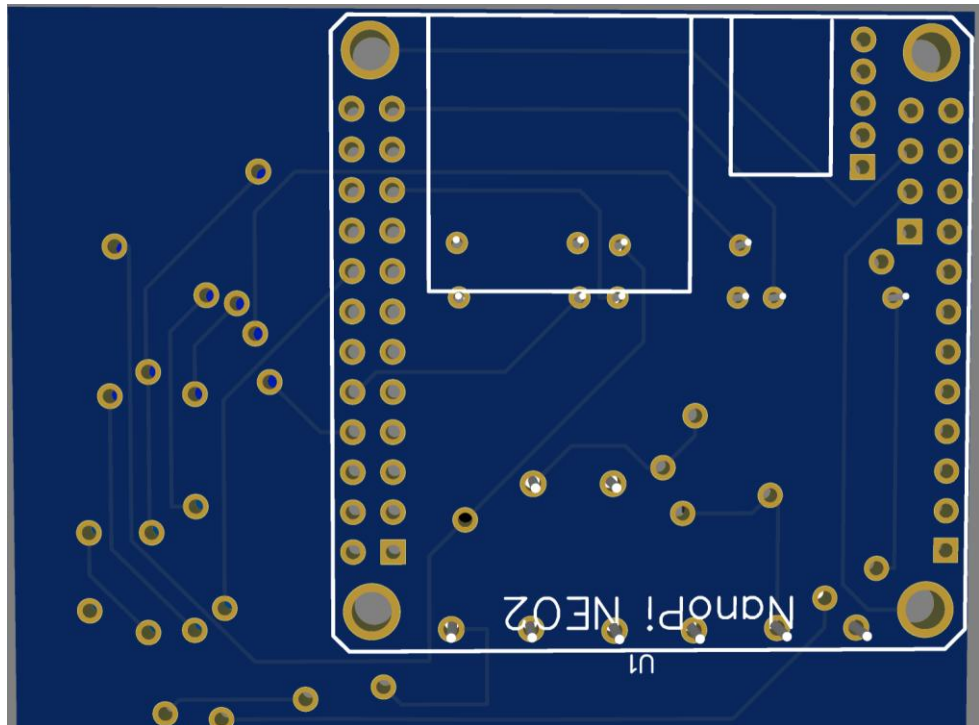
Друкована плата в 3D-вигляді (вид зверху)
